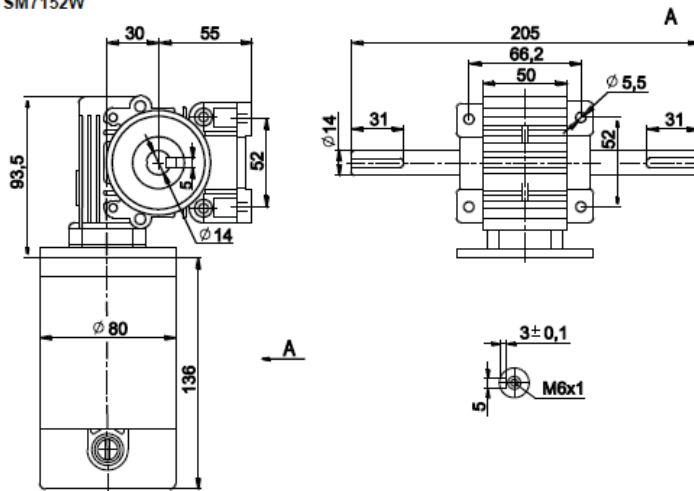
Extracto de la hoja técnica del motorreductor utilizado. Fuente: Smart Motor Devices
